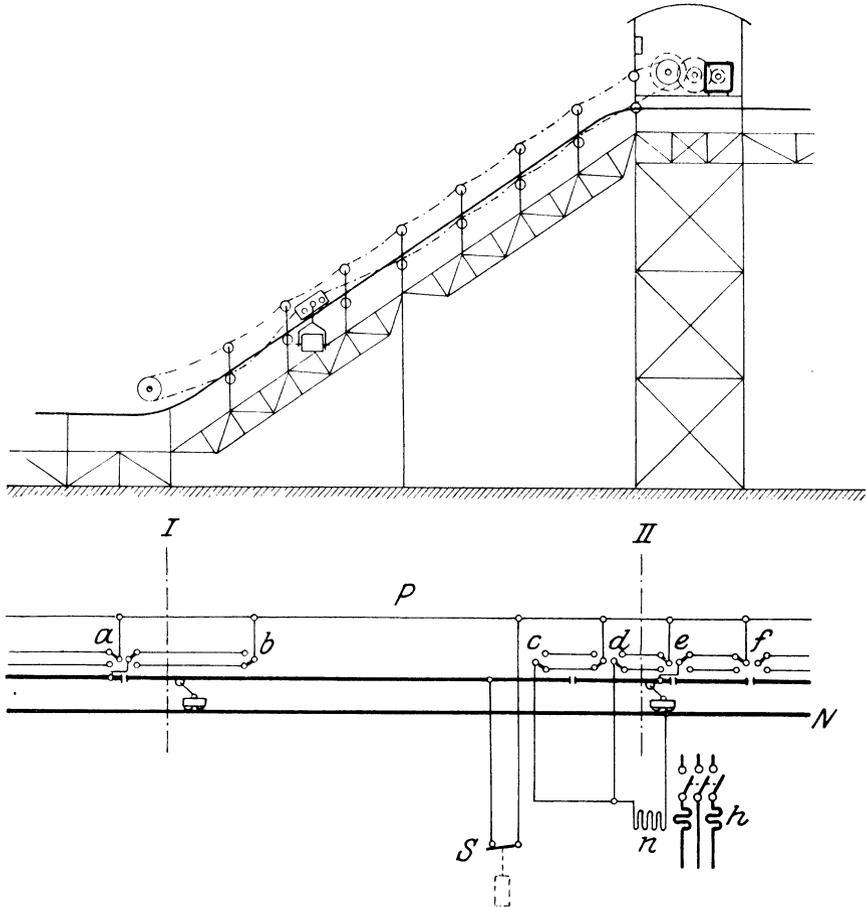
Hängebahn mit Kettenschrägaufzug.
